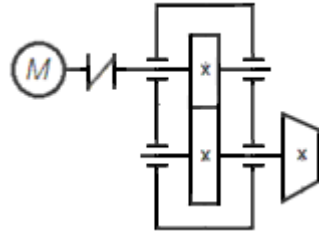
Кинематическая схема привода с открытой зубчатой конической передачей
